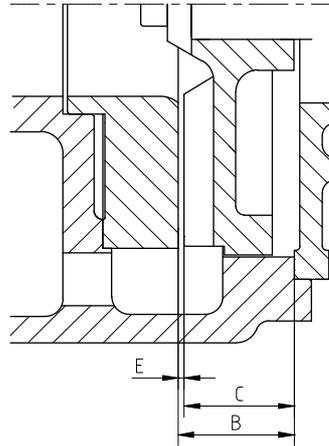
Espace entre la roue et la plaque d'usure - support de palier 1.
